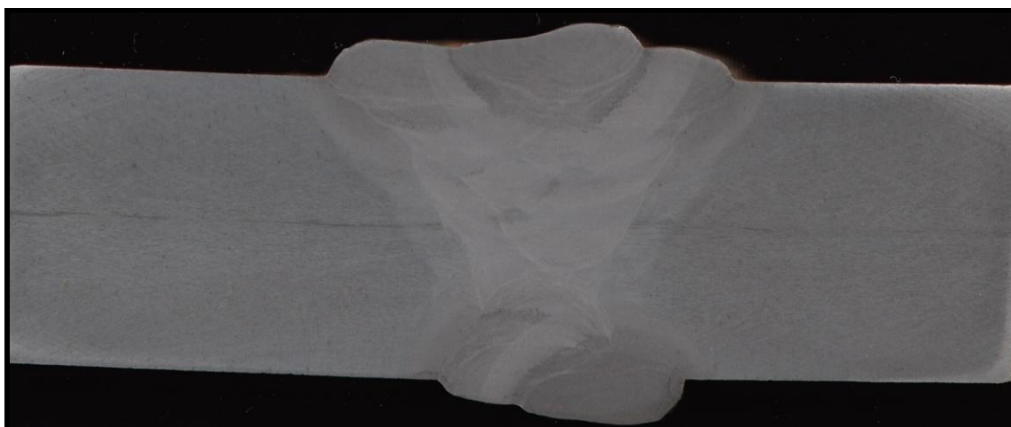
Macrografia à soldadura realizada com fio FABSHIELD XLR-8
